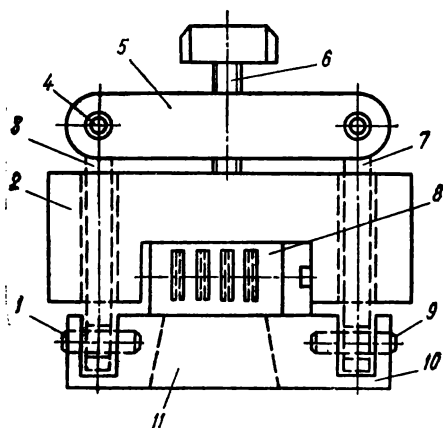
Устройство шарнирного типа для сборки магнитных головок
